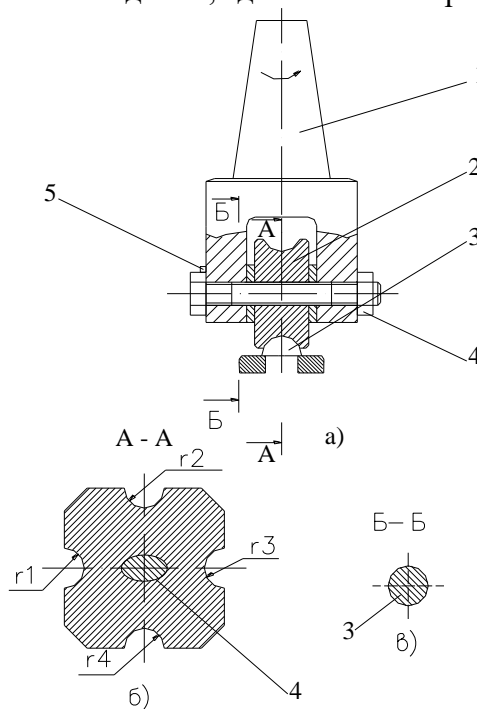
Загальний вигляд розкатника для формування чотирьох типорозмірів головок
